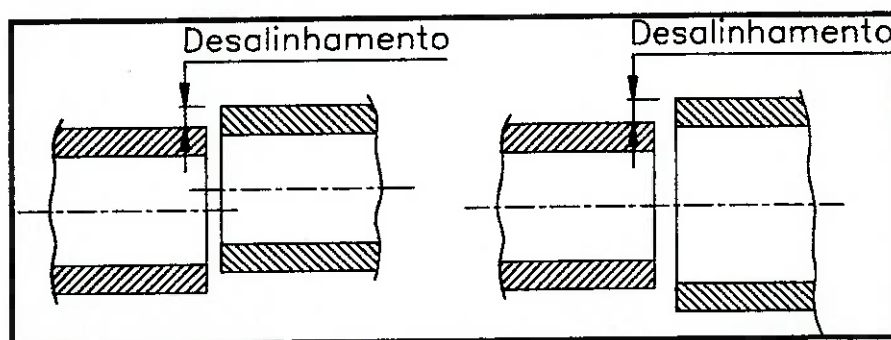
Esquema de desalinhamento entre peças na soldagem
